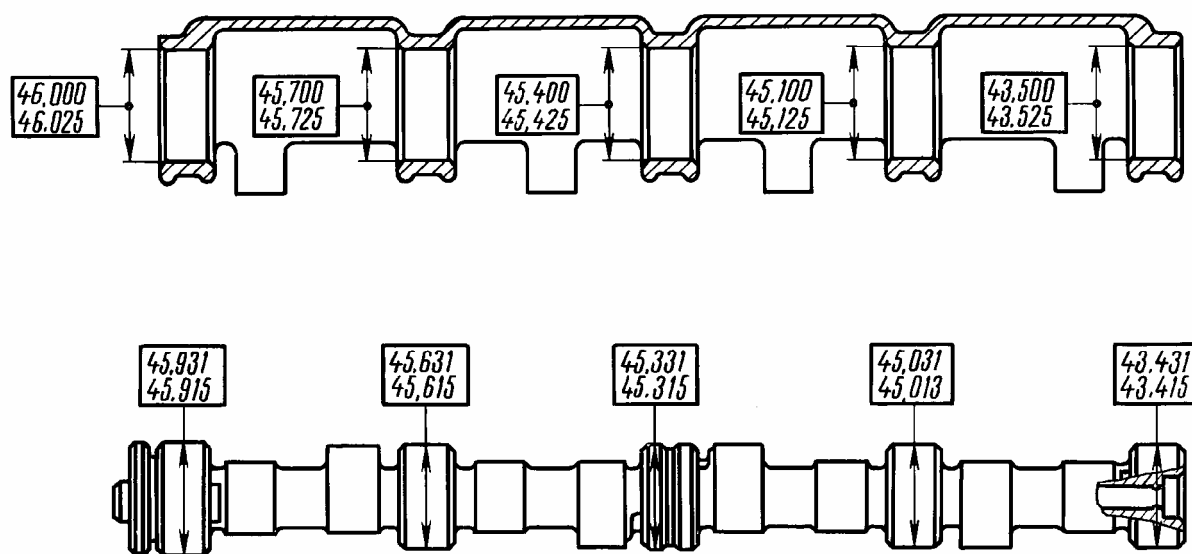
Основные размеры распределительного вала и корпуса подшипников
